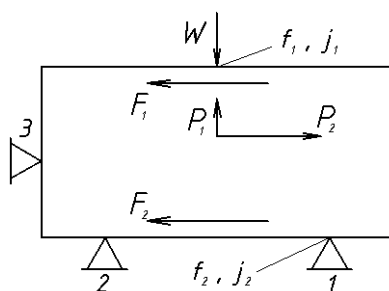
Схема действия сил обработки и зажима при установке заготовки на плоскости
